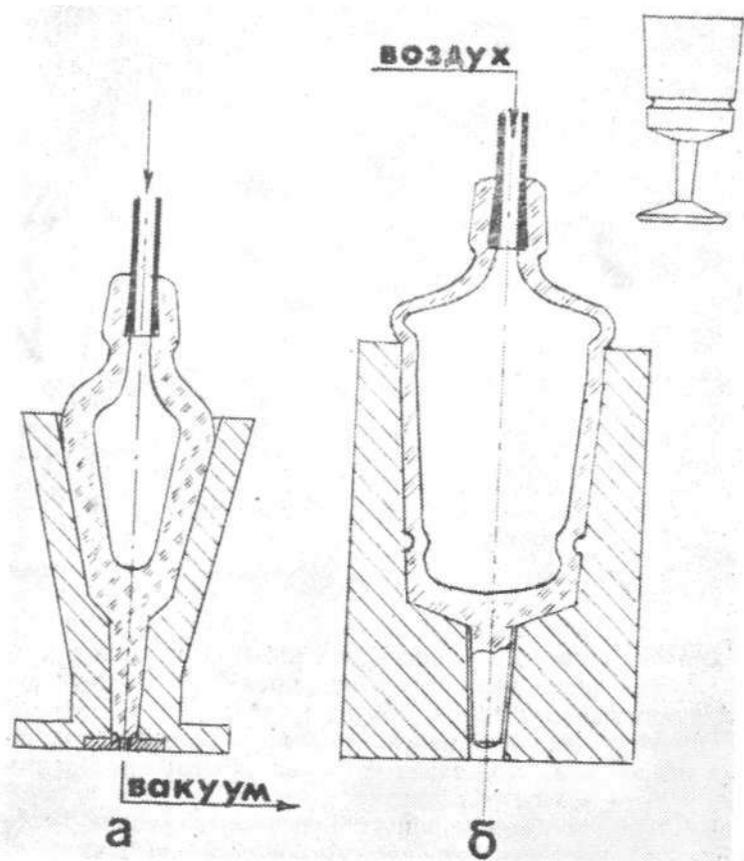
Двухстадийное изготовление рюмки с вакуумным формованием ножки.
